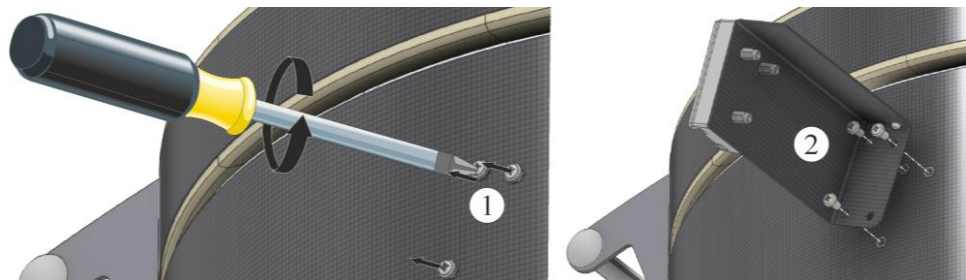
Montagem do suporte no corpo do forno (semelhante à figura)
